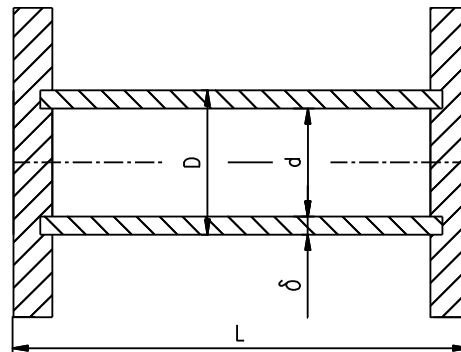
Розрахункова схема вала з фланцями.
